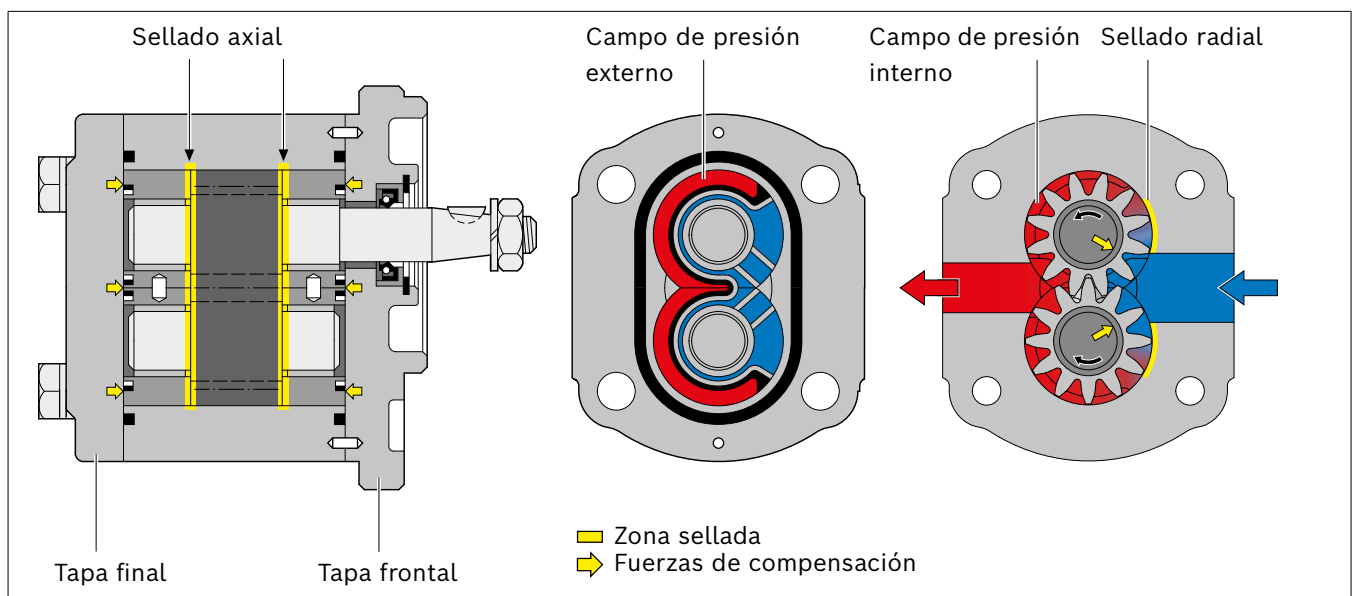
Compensación axial de la bomba a engranajes con dentado exterior
